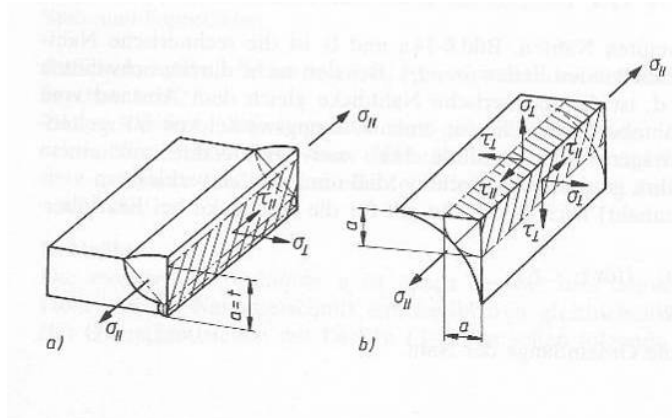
Kennzeichnung der Schweißnahtspannungen
